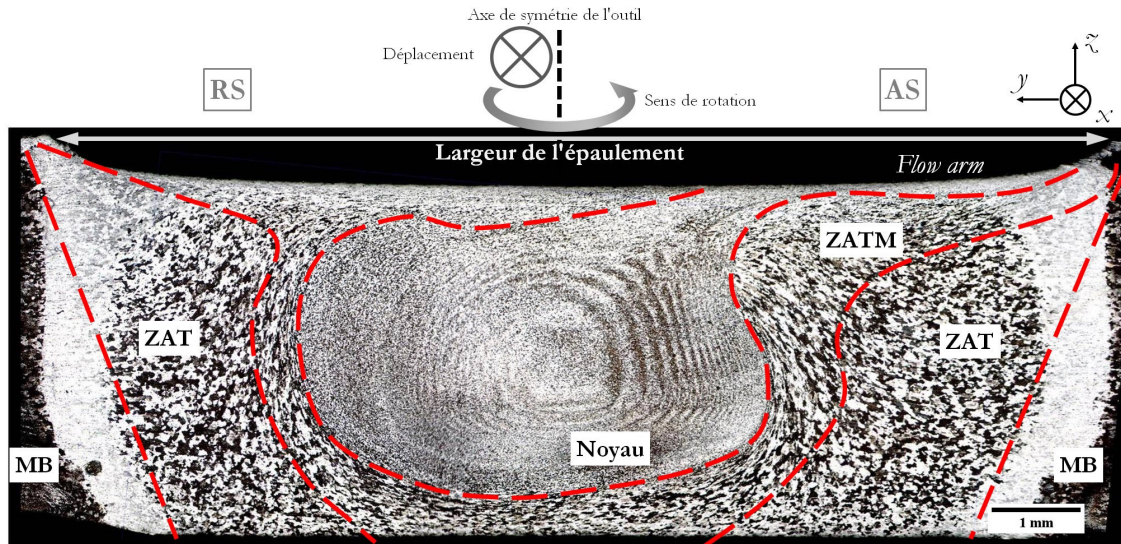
Vue en coupe d’une soudure Al-Al par friction malaxage en bout à bout perpendiculaire au trajet de l’outil.
